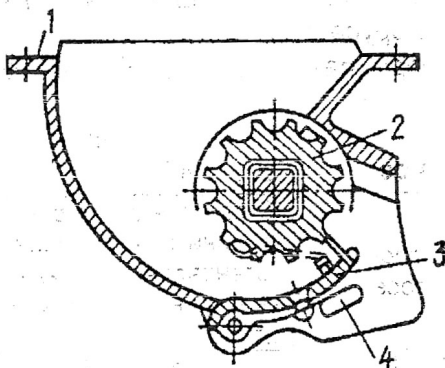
Схема расположения доньшка (поперечный разрез) катушечного высевающего аппарата с нижним высевом:
